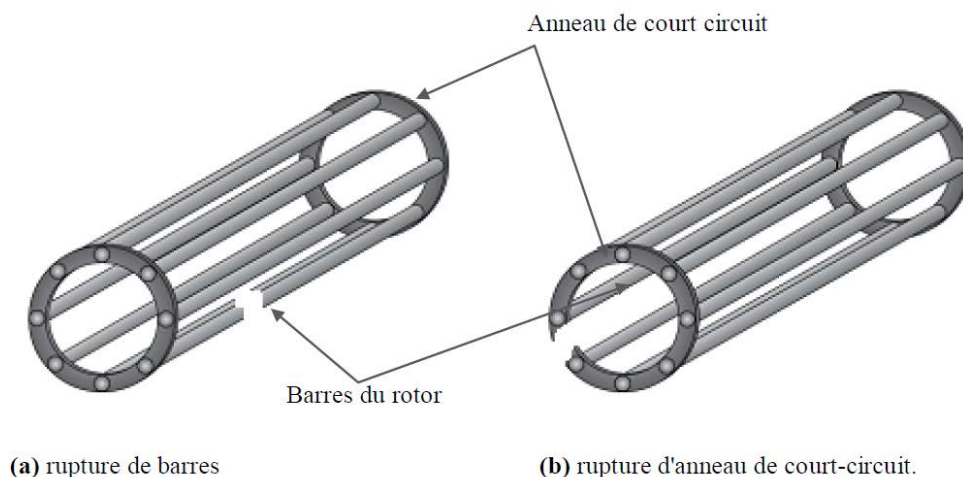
Défaut d'un rotor à cage d'écureuil.
